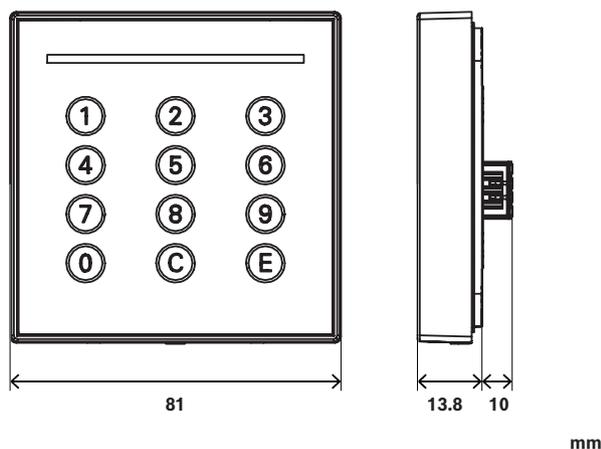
Dimensões do leitor com suporte de parede fixo
